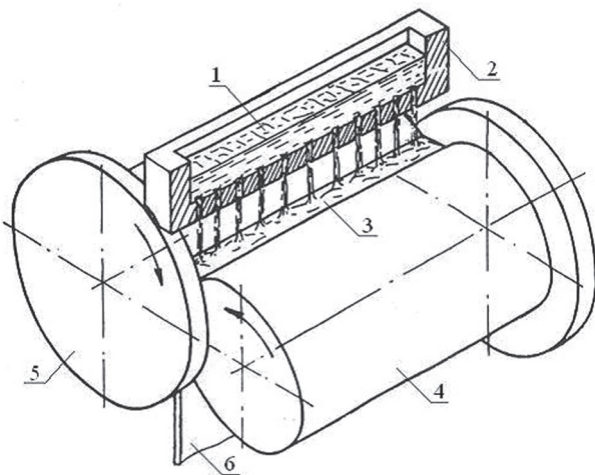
Схема непрерывного литья ленты в валковый кристаллизатор с ребордами: 1 – расплав; 2 – распределитель расплава; 3 – ванна; 4 – бочка валка; 5 – реборда; 6 – лента
